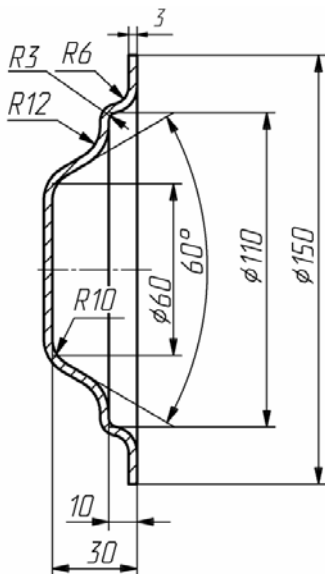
Кресленник стакана, виготовленого штампуванням
